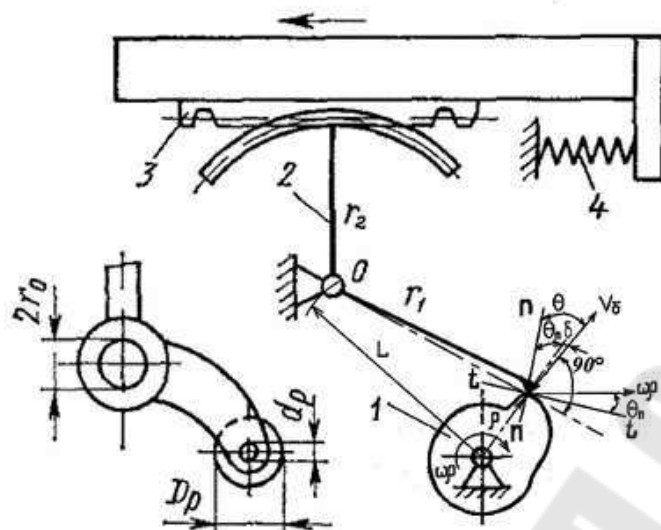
Конструктивно-кинематическая схема кулачкового механизма
